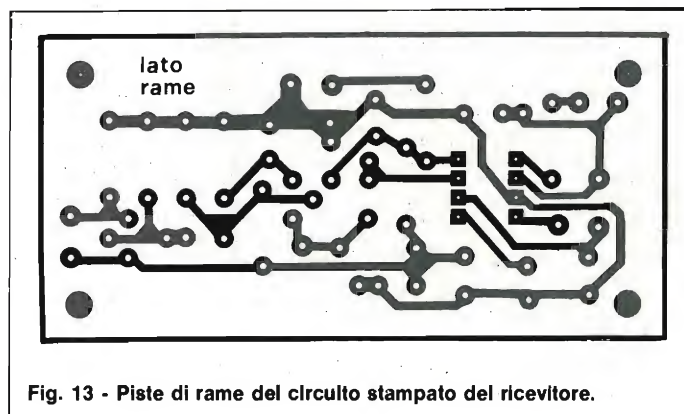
Piste di rame del circuito stampato del ricevitore.
